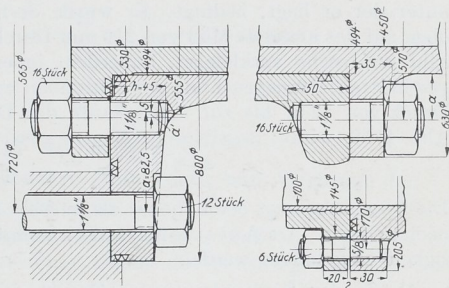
bis 1758. Flanschverbindungen am Zylinder Abb. 1755. M. 1:5. Abb. 1756. Anschluß am Rahmen und Verschraubung des vorderen Deckels. Abb. 1757. Verschraubung der Köpfe mit dem Laufzylinder. Abb. 1758. Anschluß des Zuleitungsrohres.
